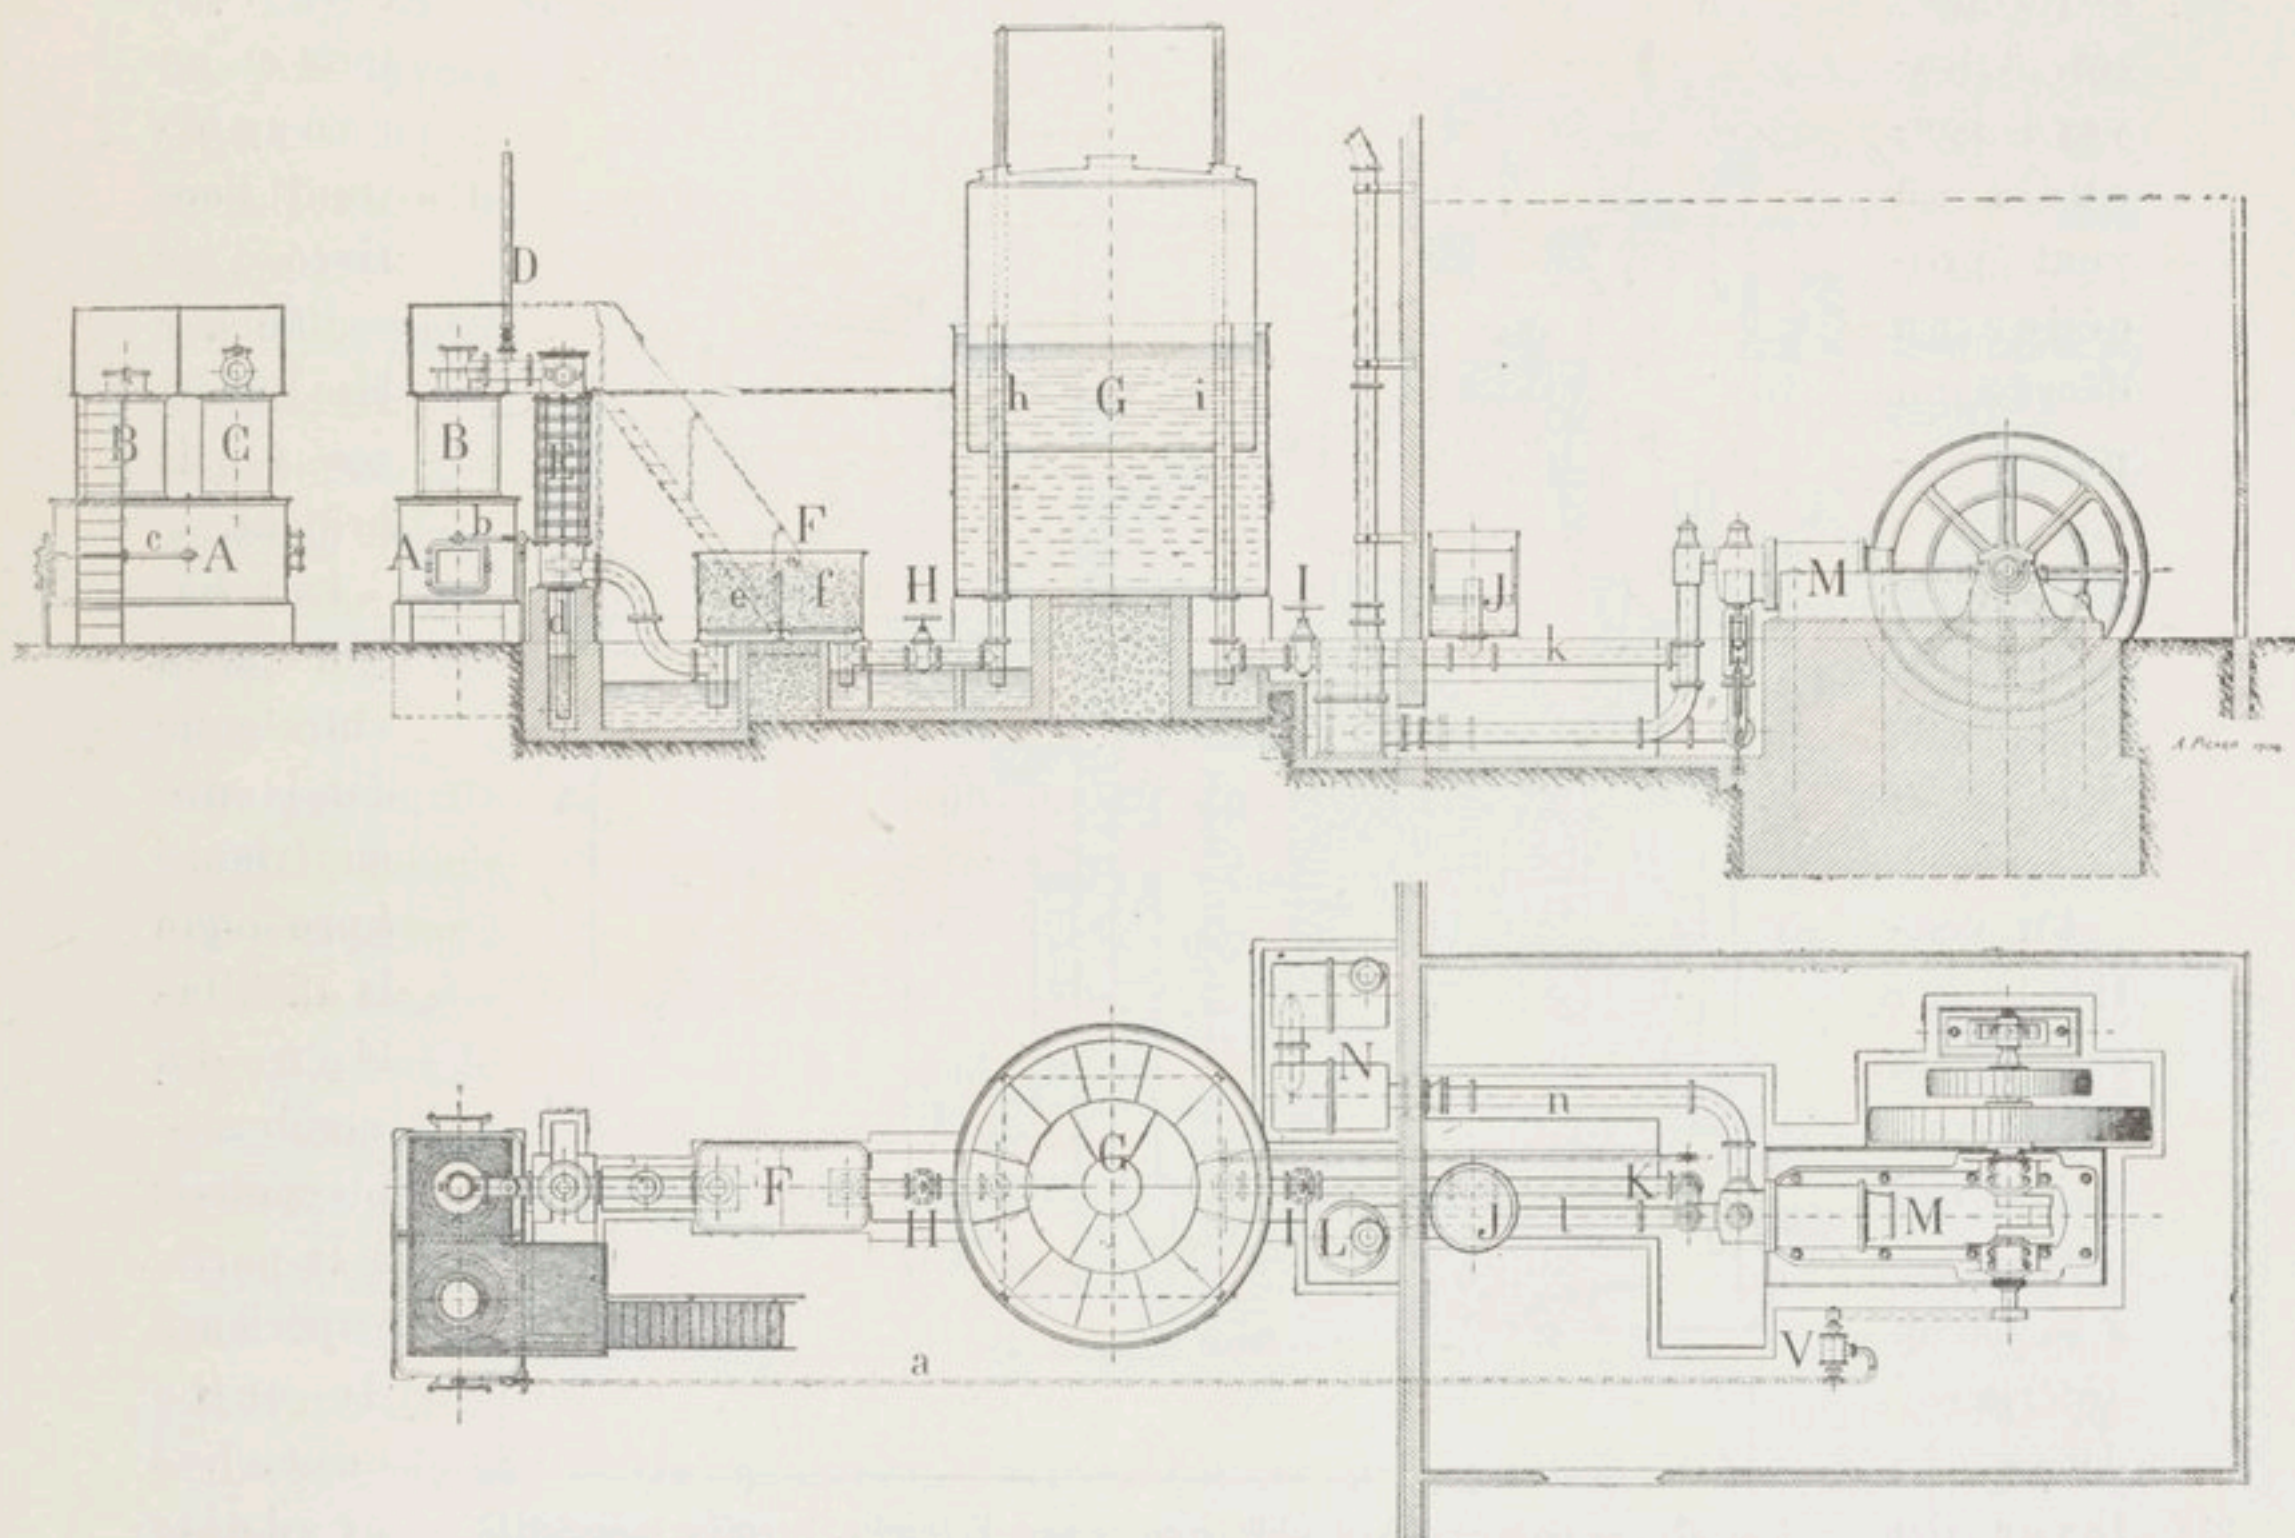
Vue d'ensemble d'une installation de gaz Riché.
